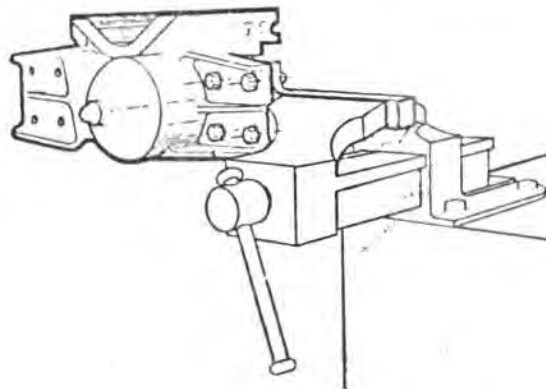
FIXATION DU CARTER ARRIÈRE DANS L'ÉTAU (8° VUE)
